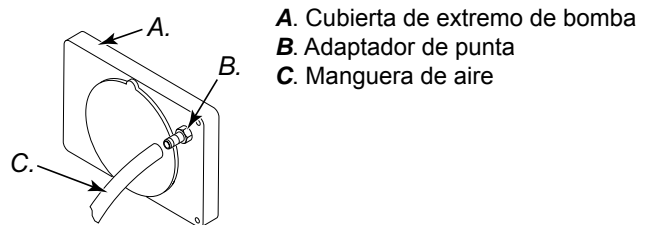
Retiro de Conjunto de boquilla/adaptador
